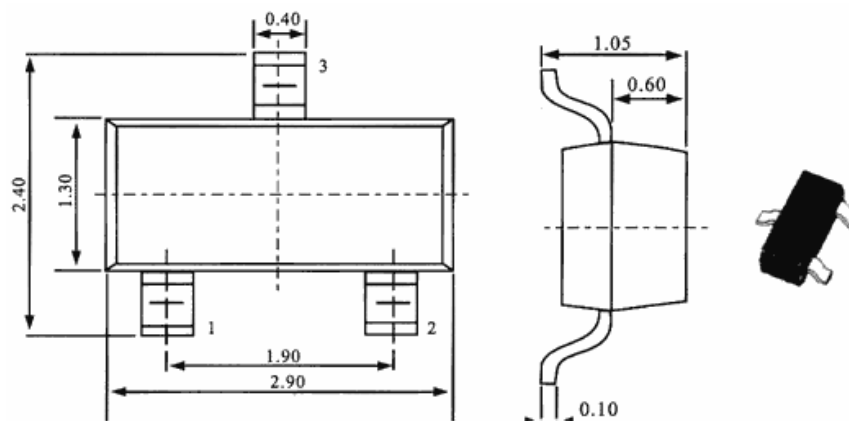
Габаритні розміри корпусу напівпровідникових елементів SOT-23
